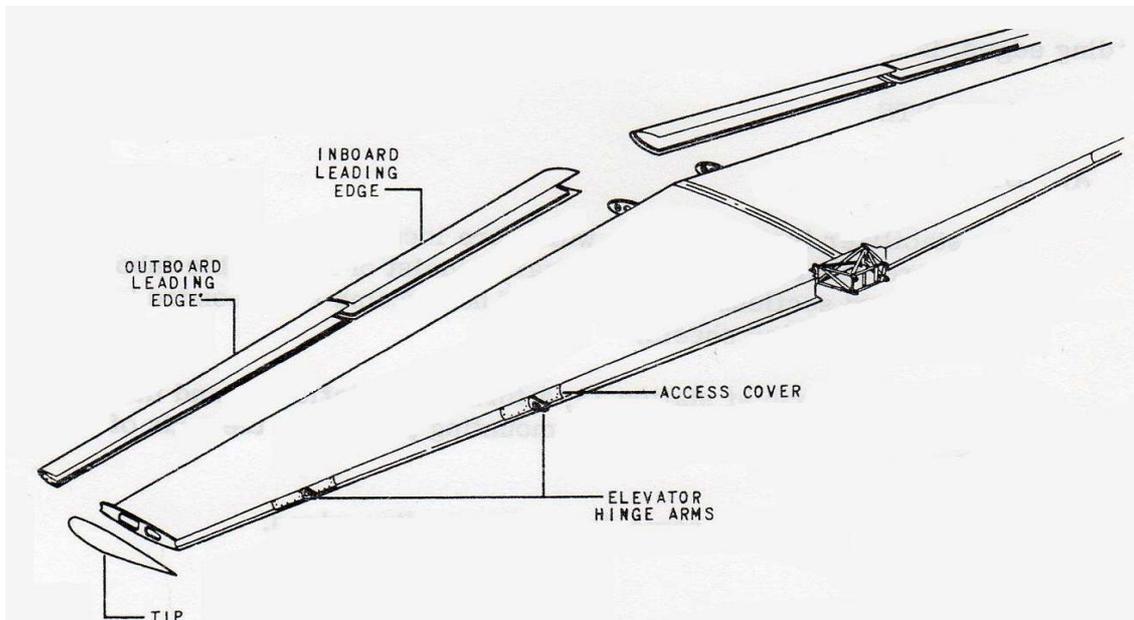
Estabilizador Horizontal Fairchild FH-227 J
